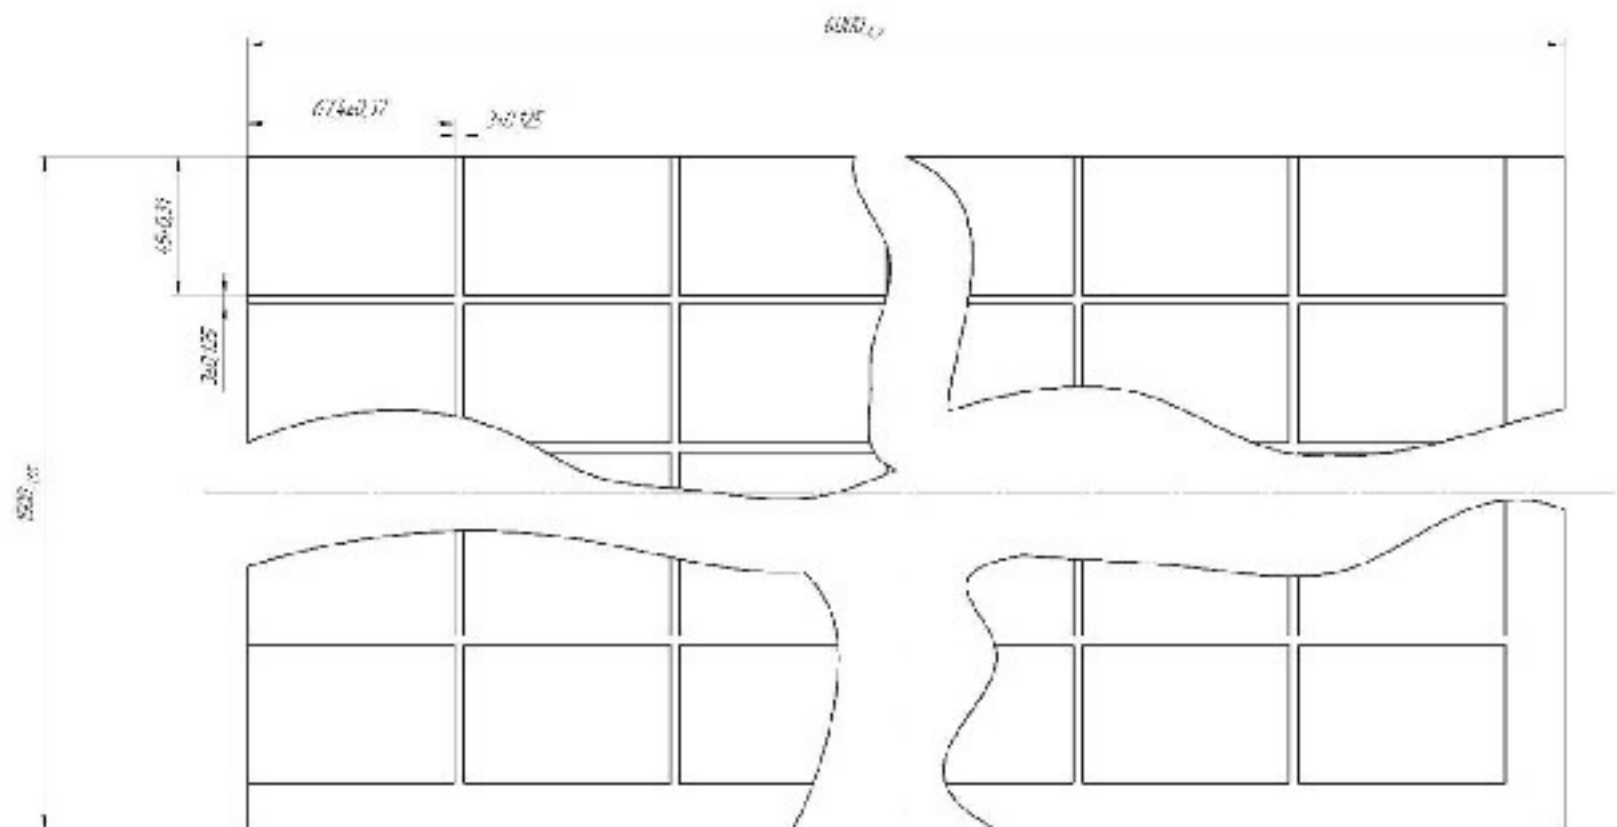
Розміщення заготовок на листовому прокаті
